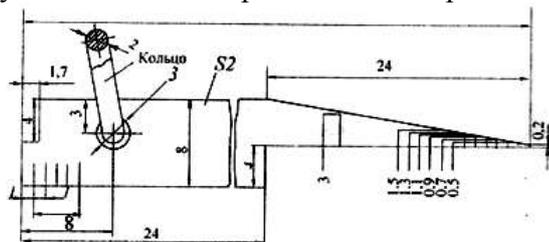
Шаблон для измерения зазора между лабиринтным кольцом и корпусом буксы.
